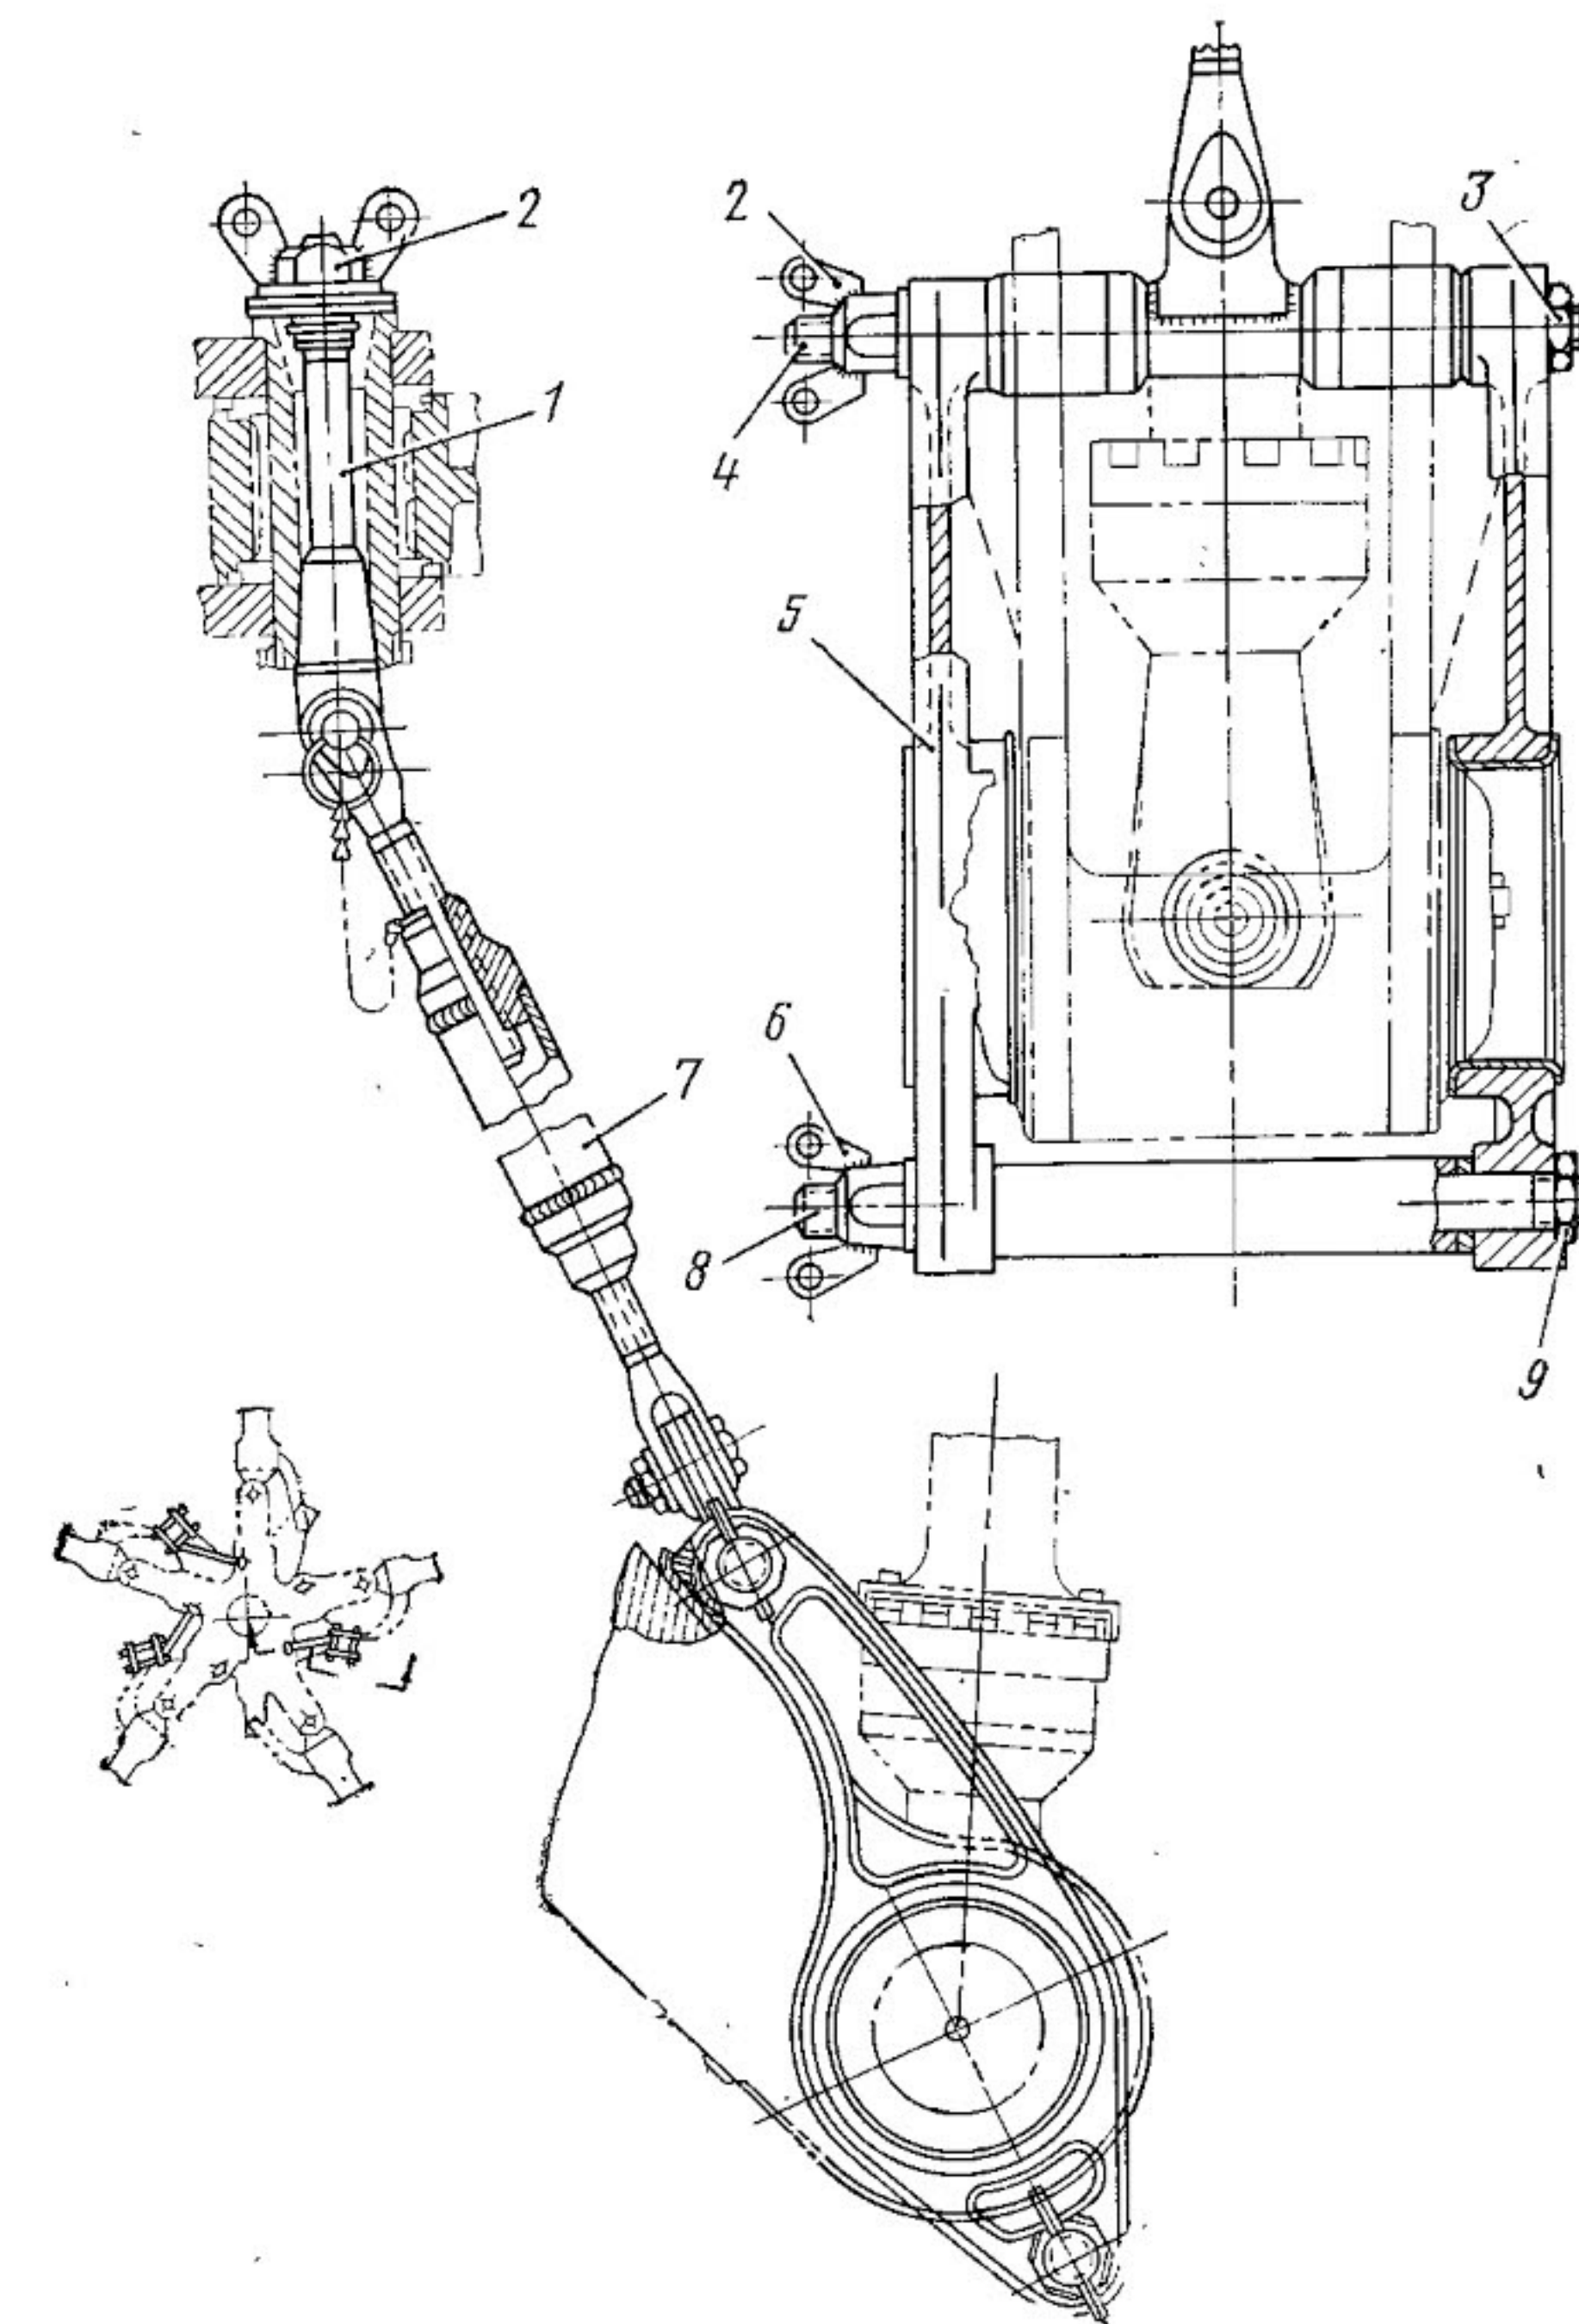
Приспособление для швартовки лопастей несущего винта в штормовых условиях:
